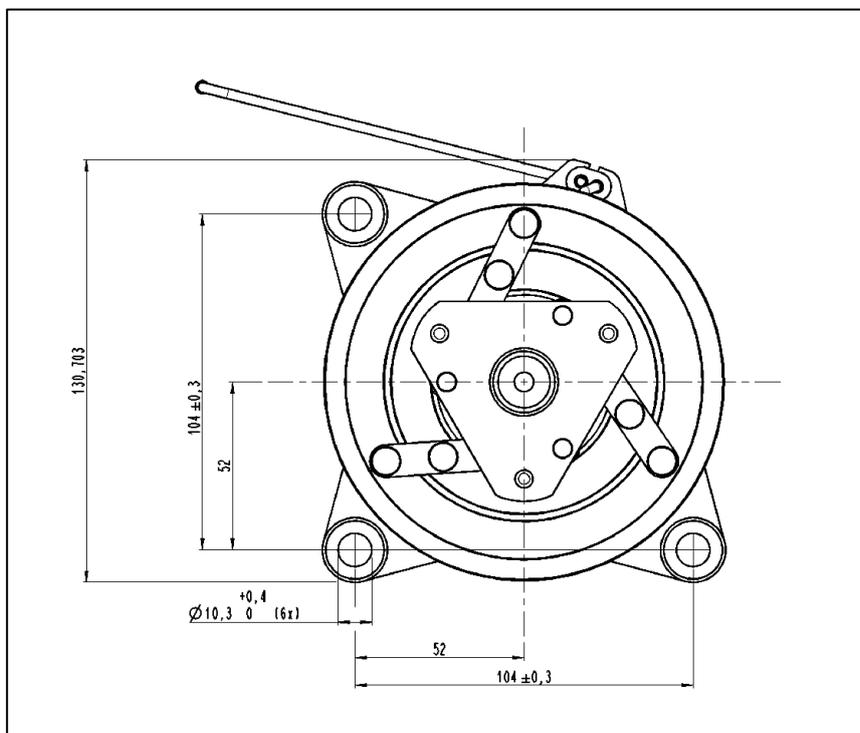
Dimensions du compresseur de climatiseur (7C0.816.803 D/E), vue avant
